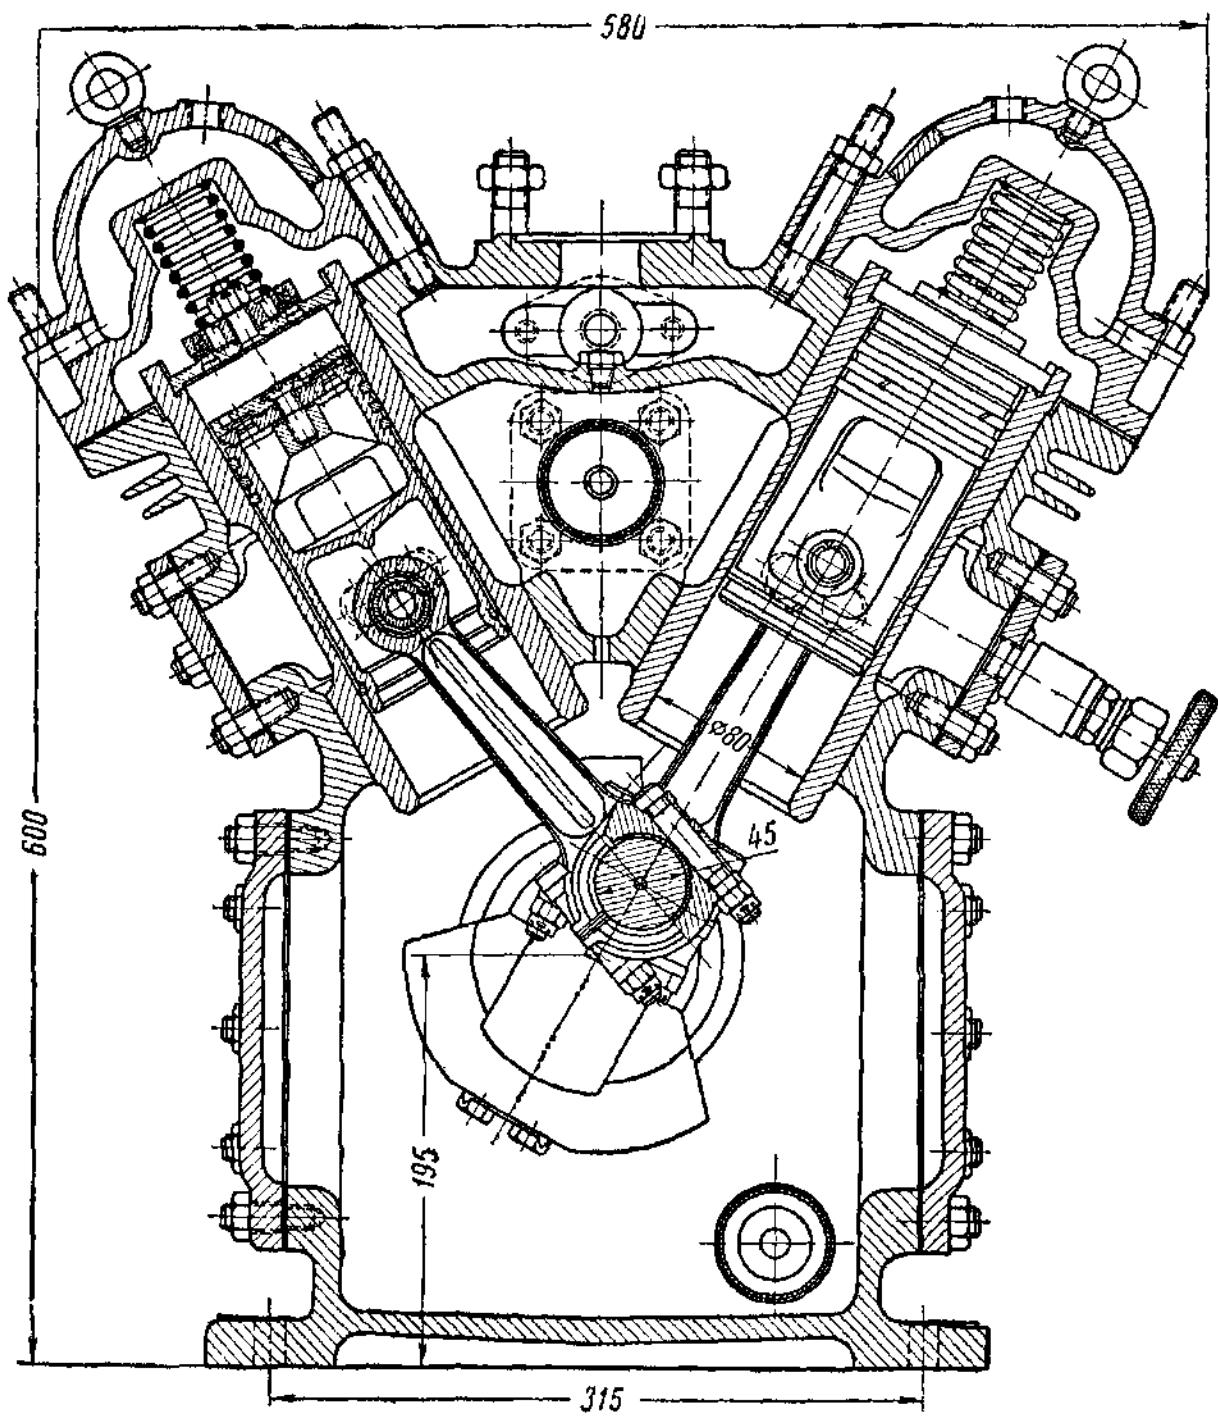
Блоккартерный четырехцилиндровый аммиачный прямоточный компрессор 4АУ-8.
